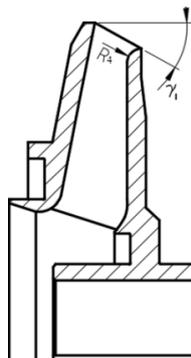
Схема обточки ведущего диска рабочего колеса и скругление кромки для первой схемы
